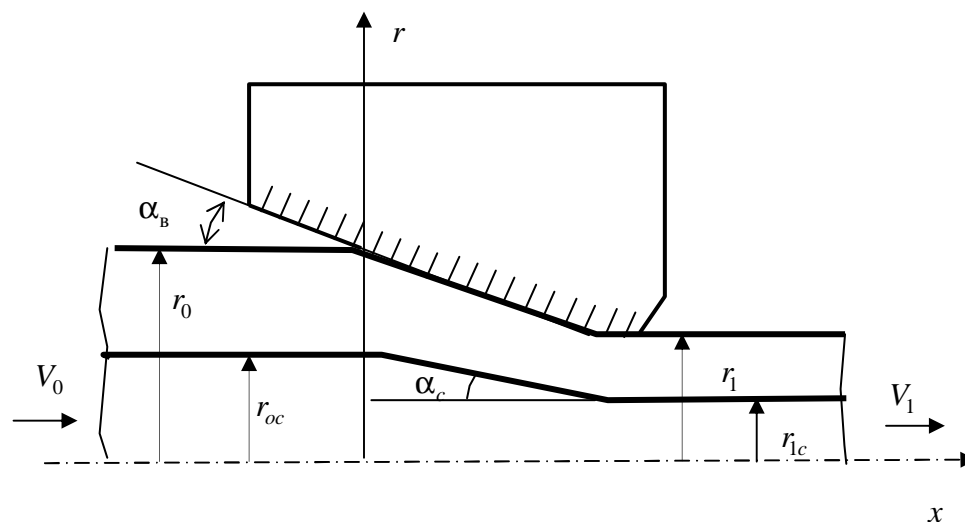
Схема деформирования двухкомпонентной композитной заготовки в конической матрице
